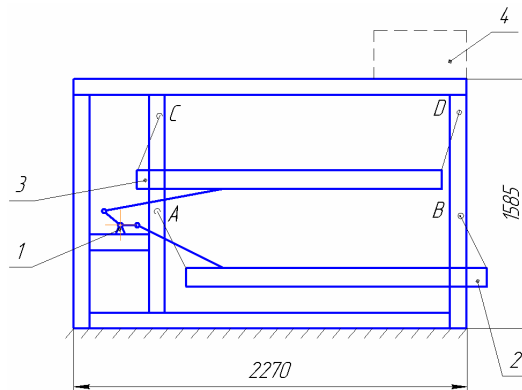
Несущая конструкция зерноочистительной машины: 1- приводной механизм; 2, 3- ситовые корпуса; 4- аспирационная система
